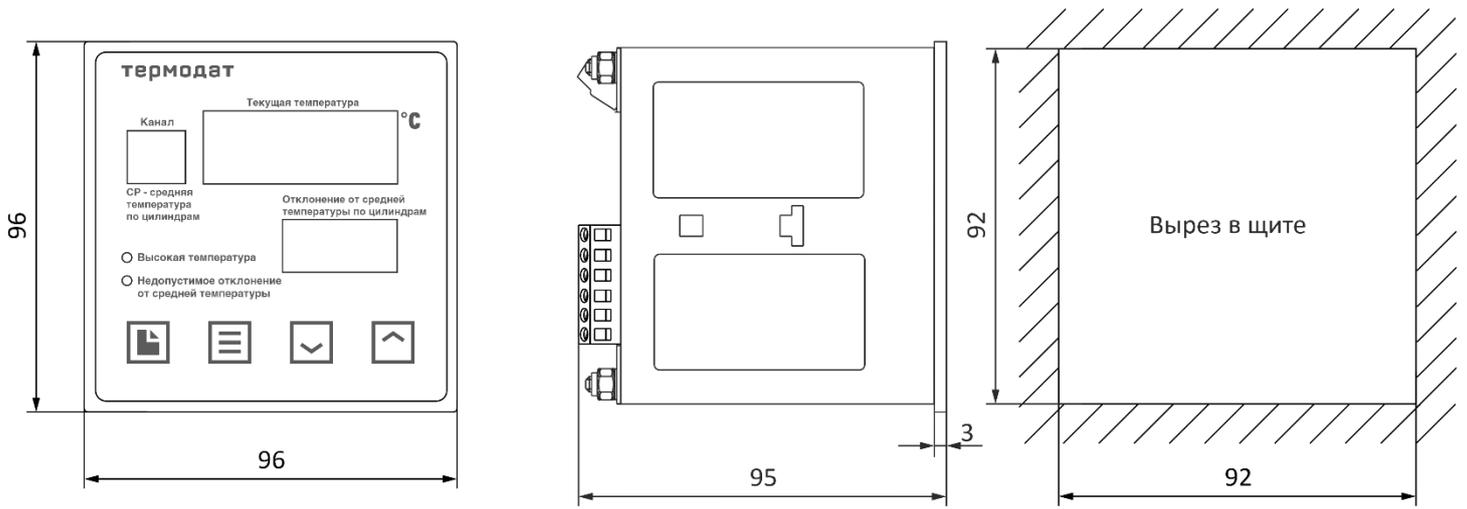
Габаритные размеры основного блока и блока индикации
